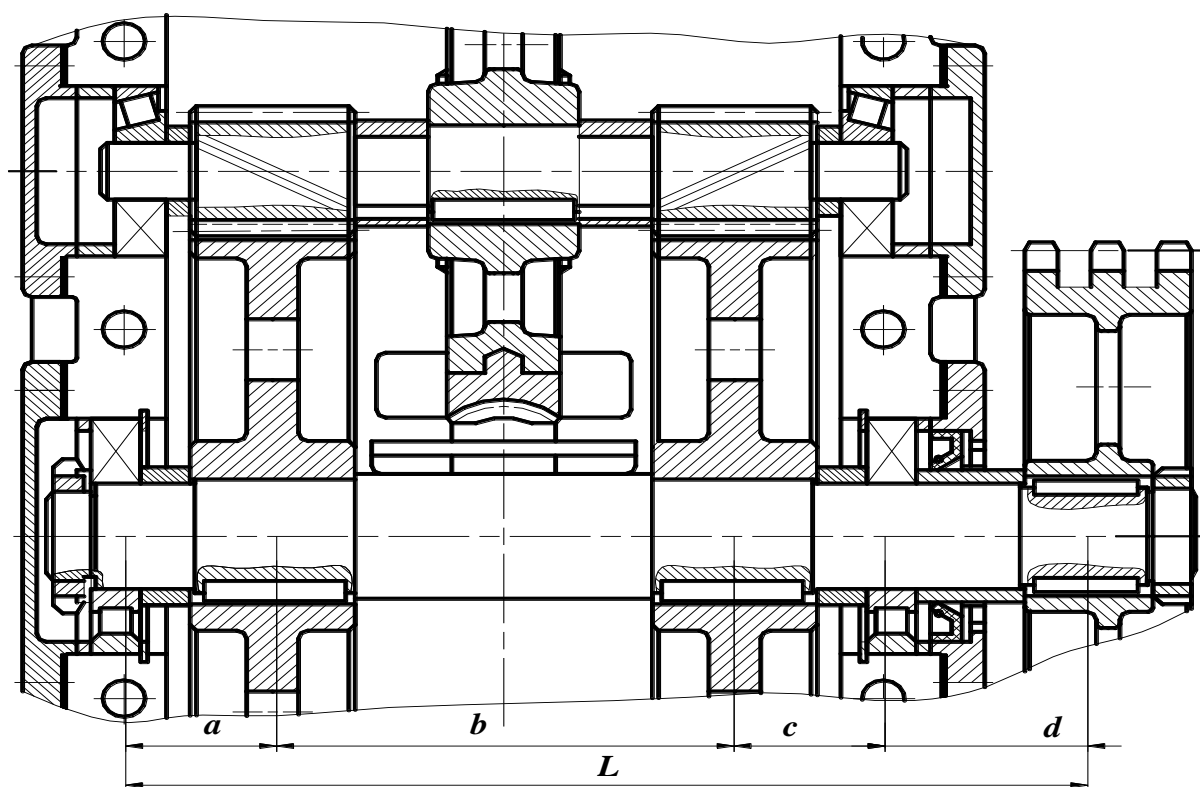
«Плаваючий» вал шевронної передачі
